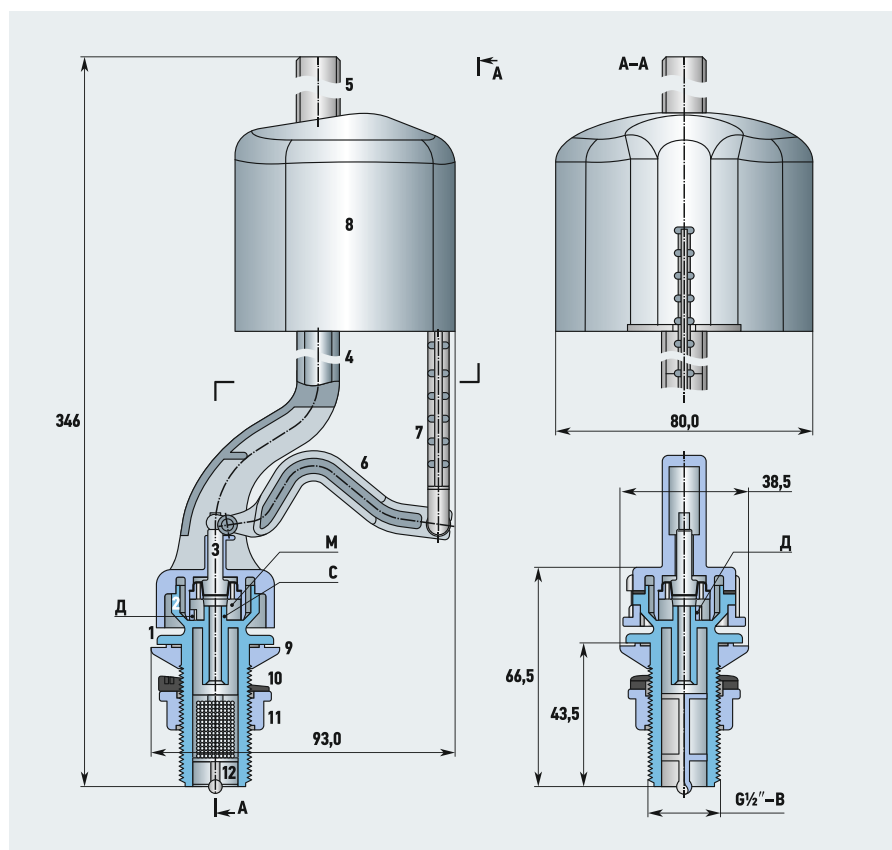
Конструкция новой наполнительной арматуры противодействия нижней подводки (1 — штуцер; 2 — манжета чулочного типа; 3 — шток; 4 — стойка-дефлектор; 5 — удлинитель стойки; 6 — рычаг; 7 — тяга; 8 — поплавок; 9 — эластичная конусная прокладка; 10 — косая шайба; 11 — гайка; 12 — фильтр грубой очистки; 13 — тяга)
